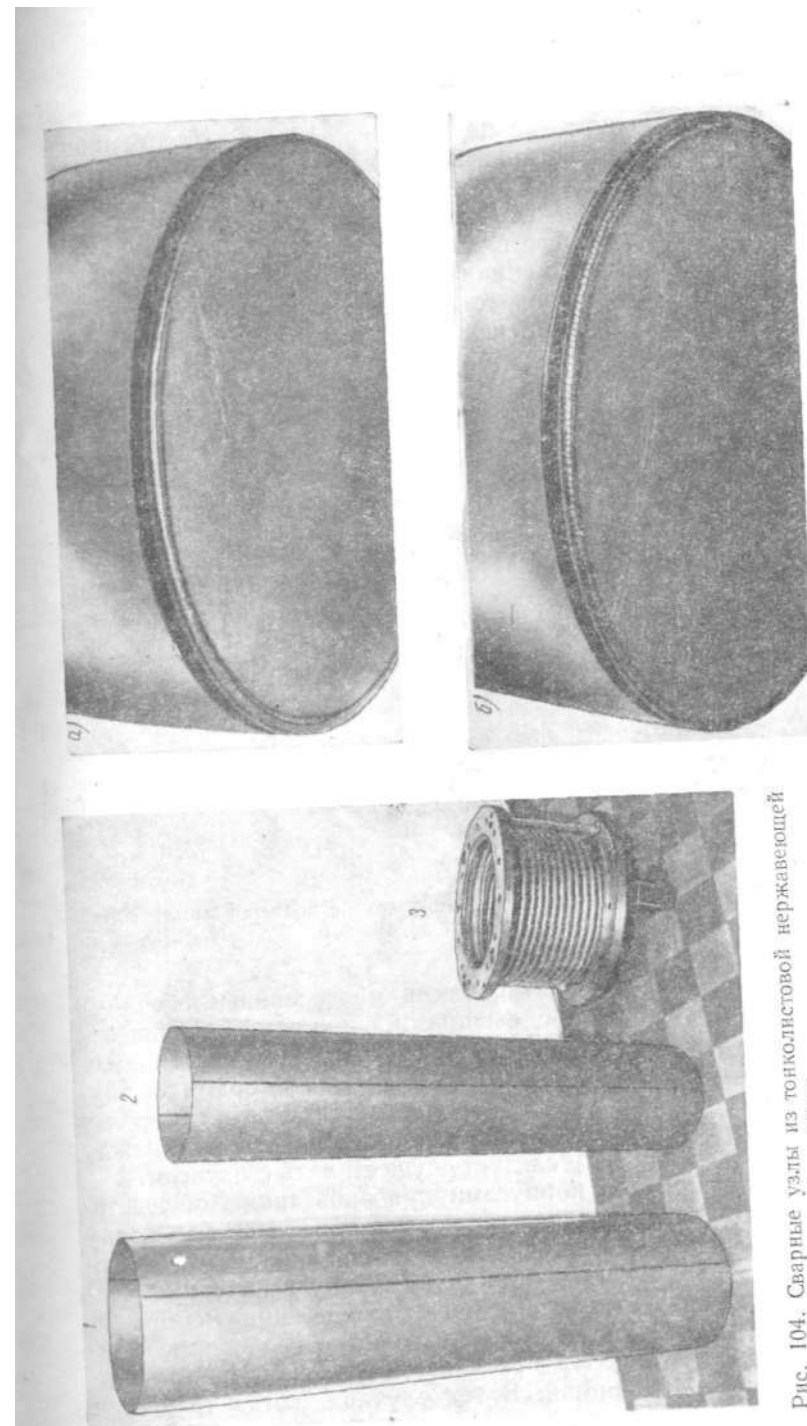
Сварные узлы из тонколистовой нержавеющей стали.
